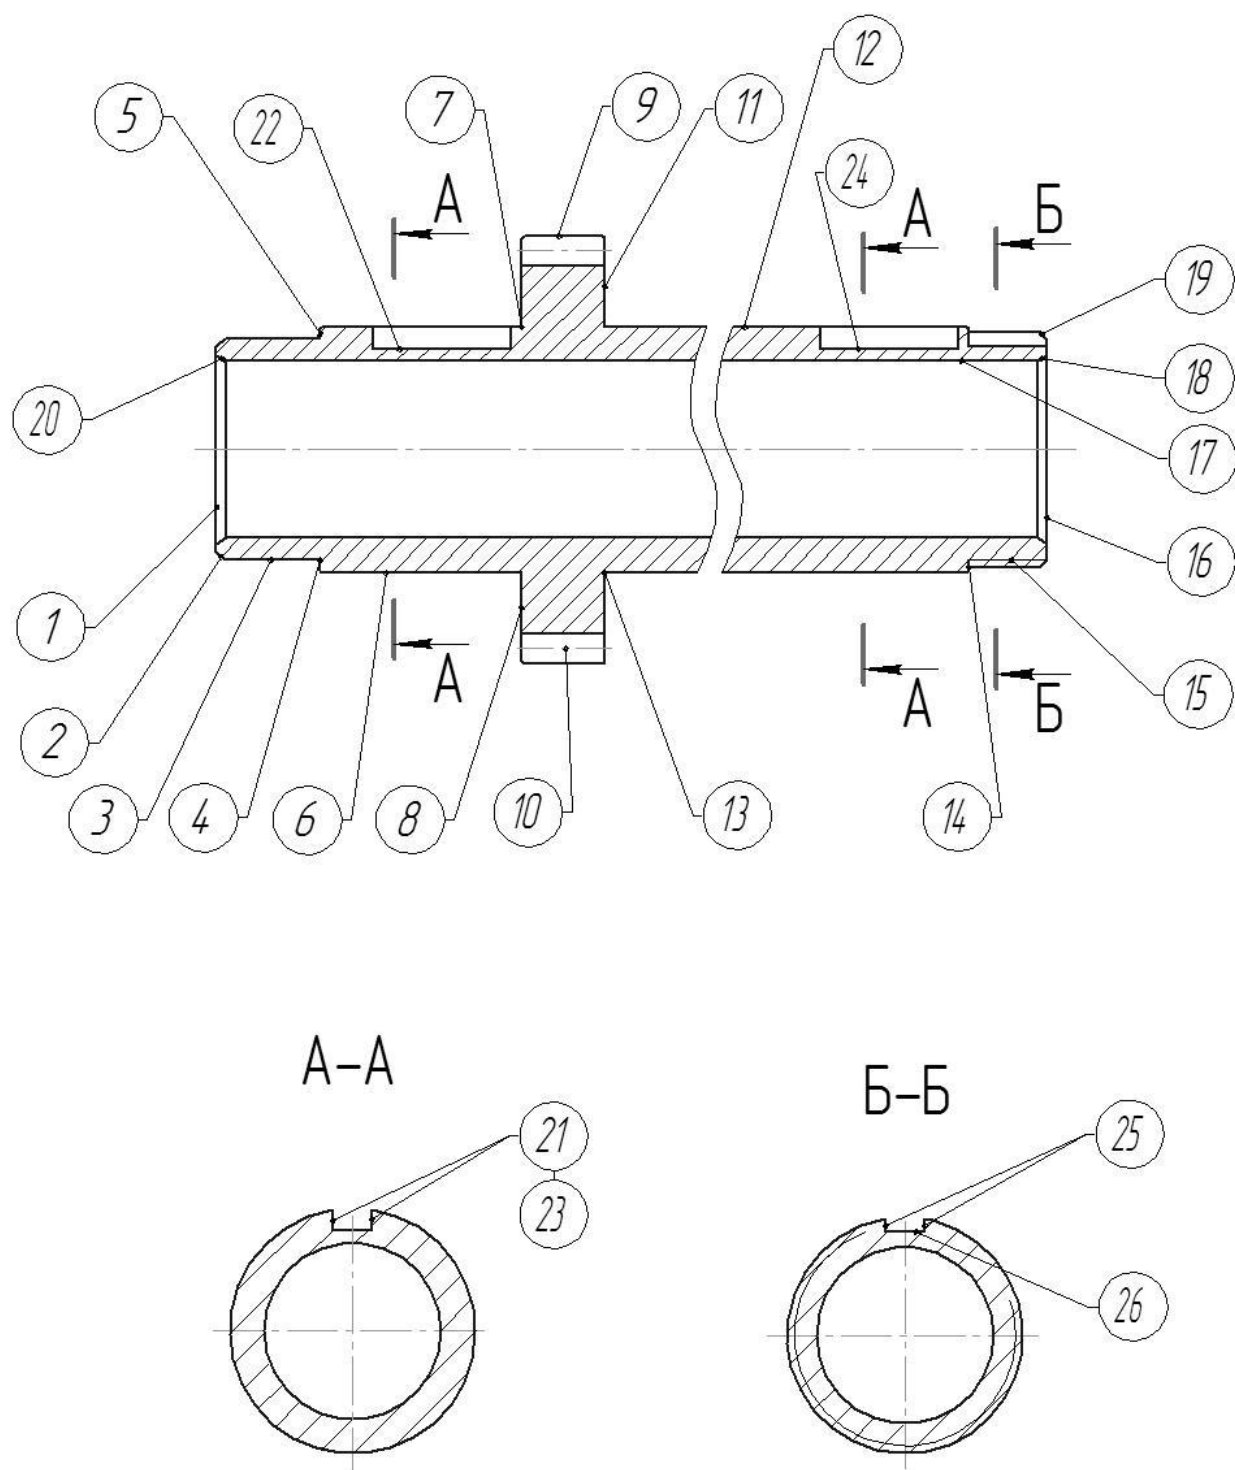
Классификация поверхностей детали вал-шестерни редуктора двухшнекового экструдера
